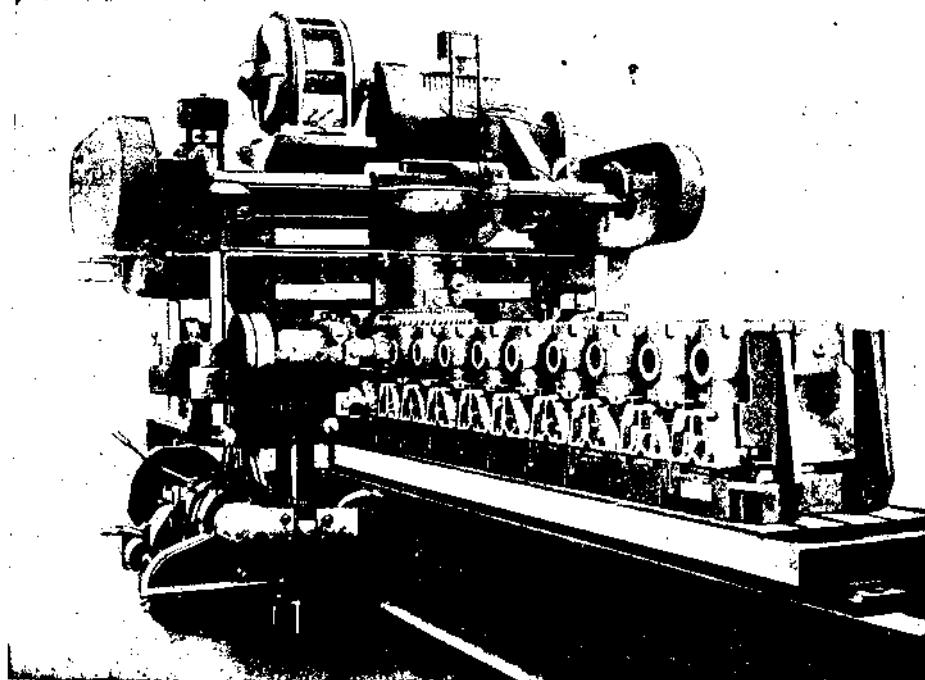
Другой вид продольно-фрезерного станка Ингерсоль.
